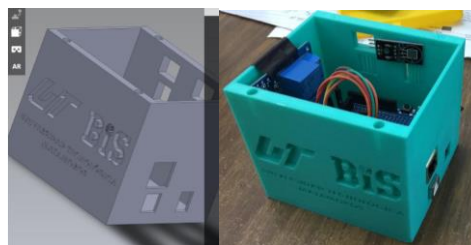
visualización de diseño modelado en ·3D de carcasa y posteriormente si impresión en 3D
